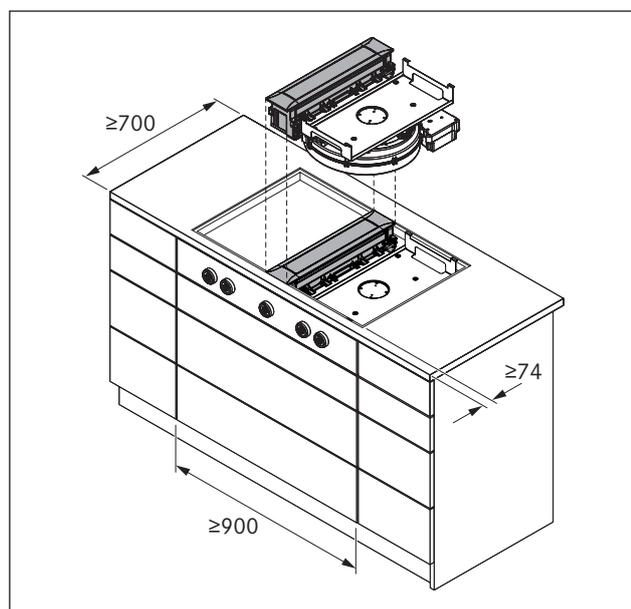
Medidas de montagem do aparelho PKA e PKAS, PKASAB
